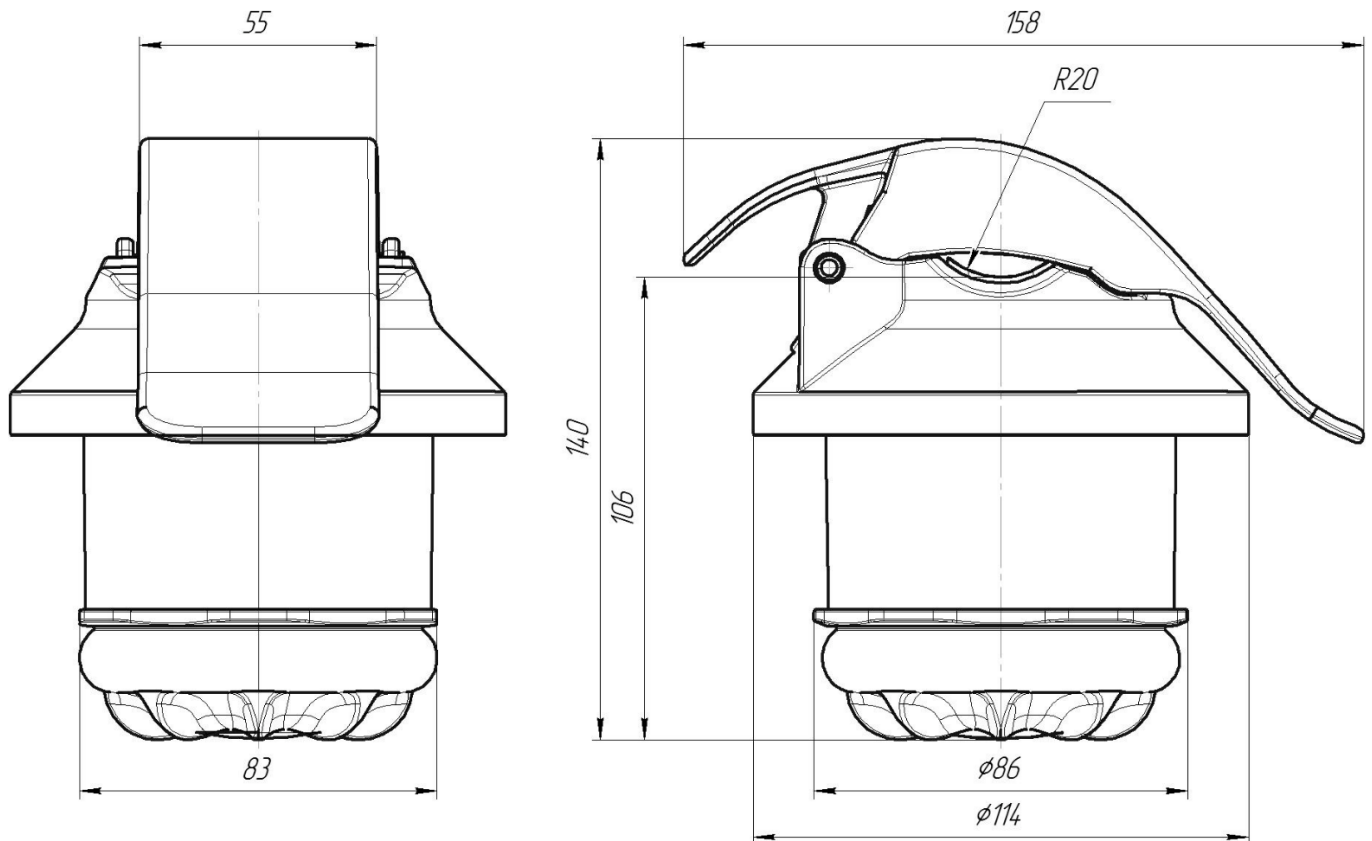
Габаритные размеры индикатора ИКЗ-В34
